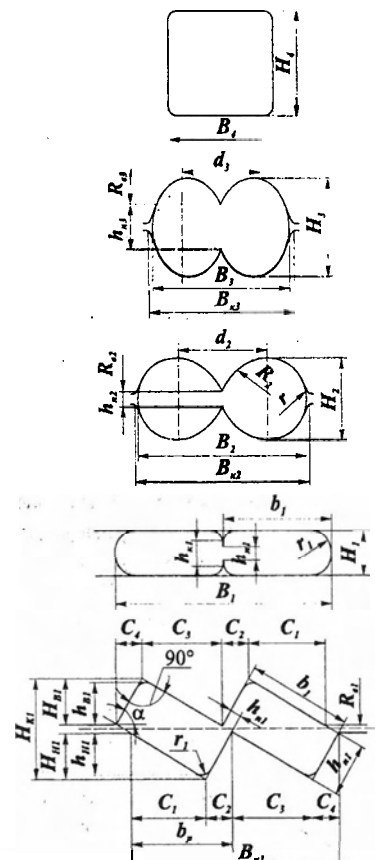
Схема калибровки валков для двухручьевой прокатки-разделения сортовых профилей с продольным разделением раската в двухручьевом калибре с наклонными ручьями к осям валков.
